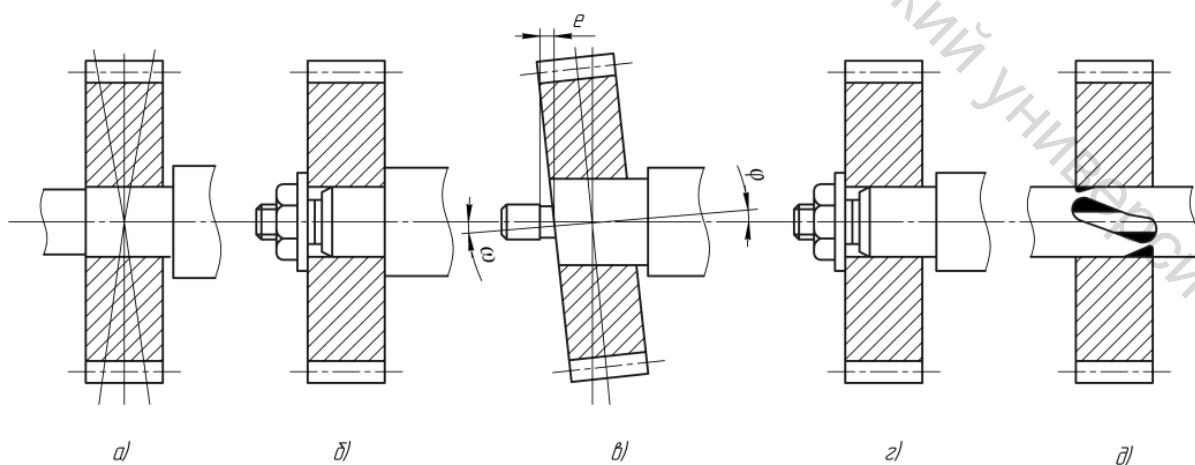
Погрешности установки зубчатых колес на валу
